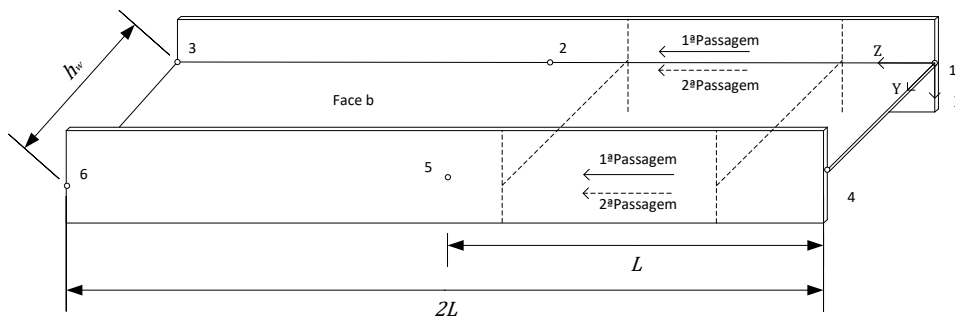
Definição dos eixos globais da chapa durante o processo de soldadura
